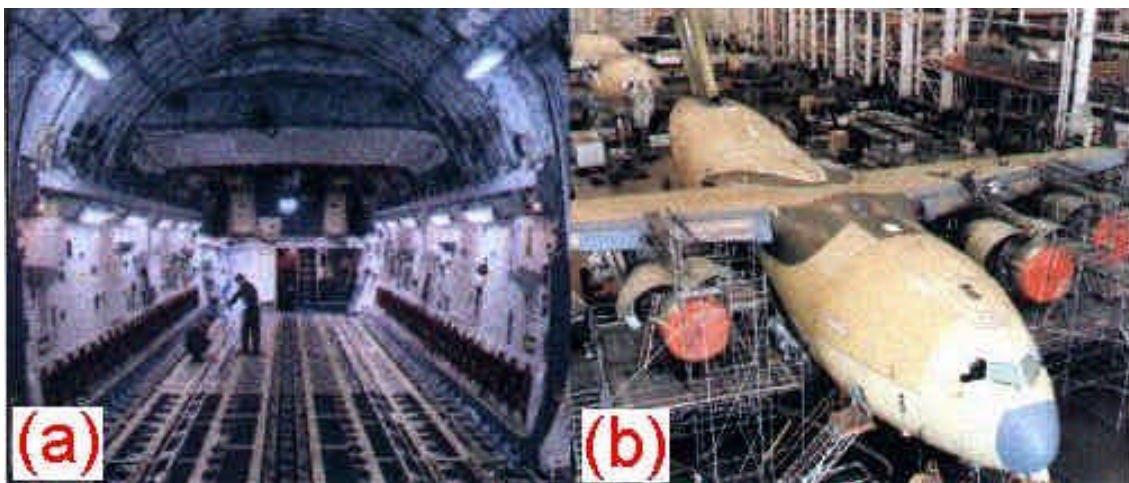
(a) Detalhe do piso de carga usinado a partir de placa 7050-T7451. (b) Detalhe da linha de montagem do Boeing C-17 Globemaster. Adaptado de [56].
